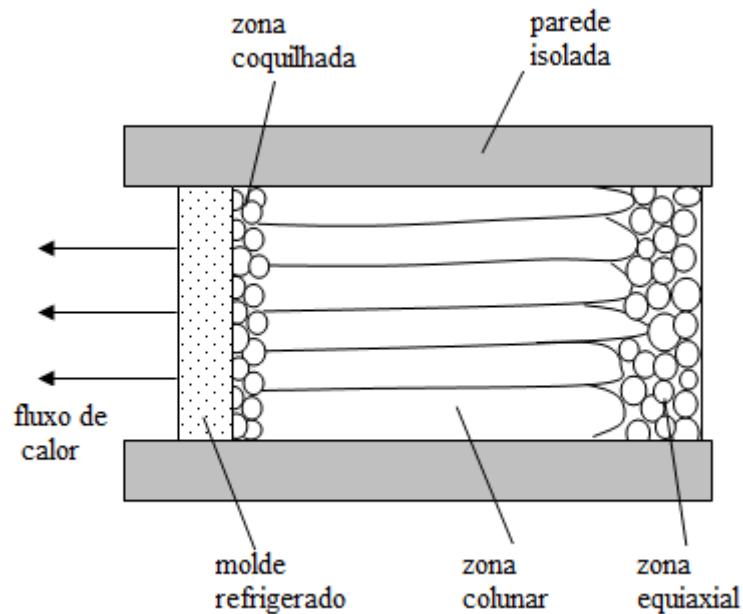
Representação esquemática das estruturas coquilhada, colunar e equiaxial (Santos, 2006)
